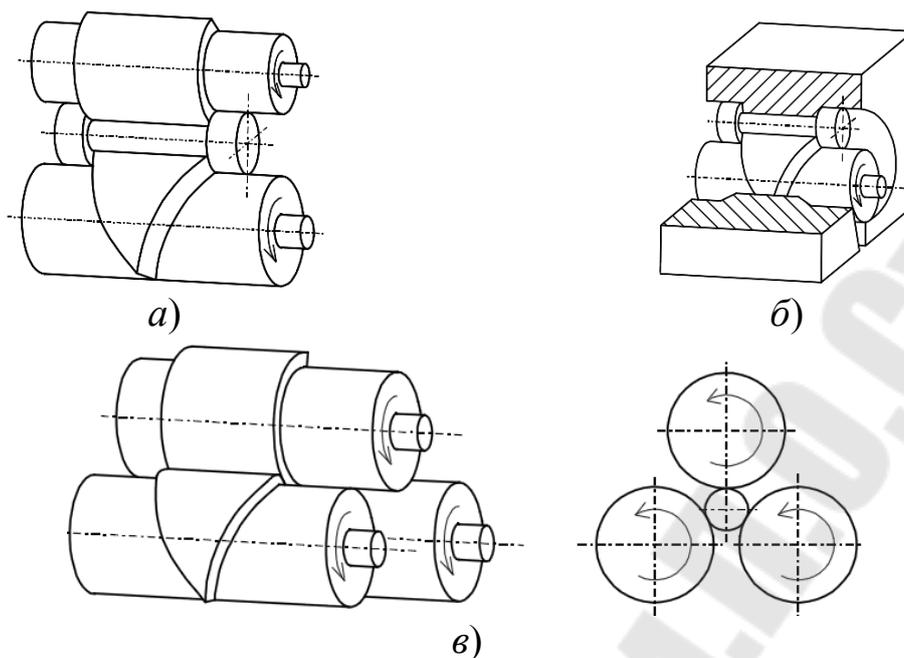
Основные компоновки станов валковой поперечно-клиновой прокатки:
